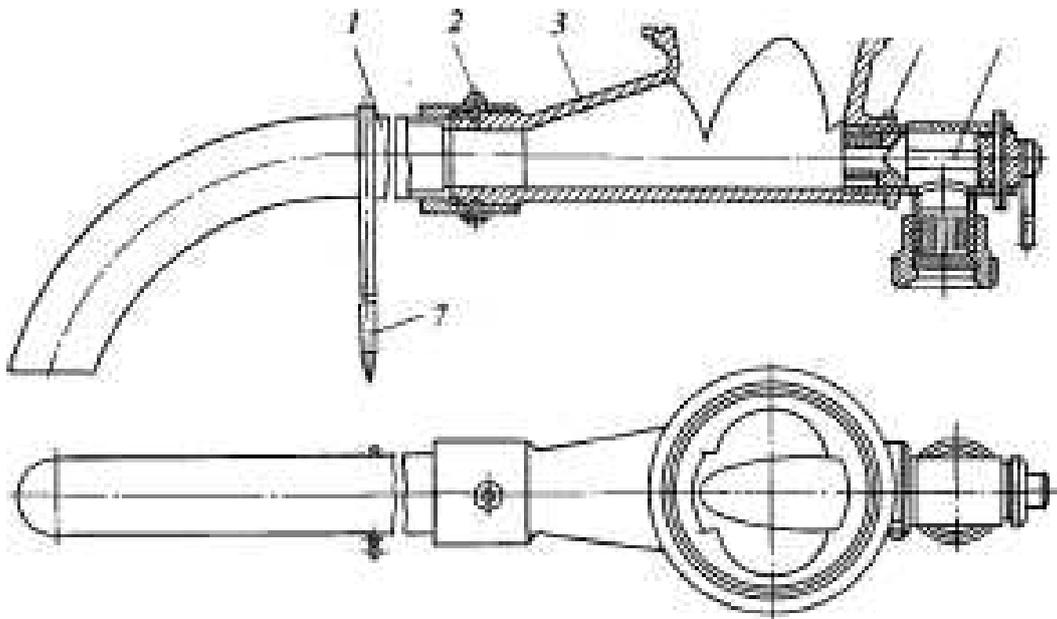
Смесительное устройство: 1 – сборный ствол; 2 – зажимной болт; 3 – корпус смесителя; 4 – щелевидные поворотные насадки
